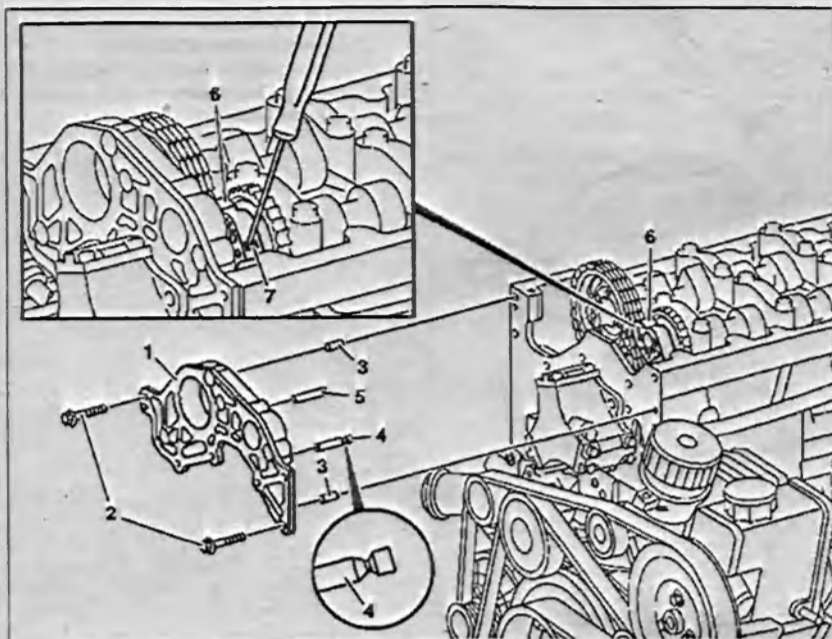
Снятие и установка передней крышки на головке блока цилиндров:
